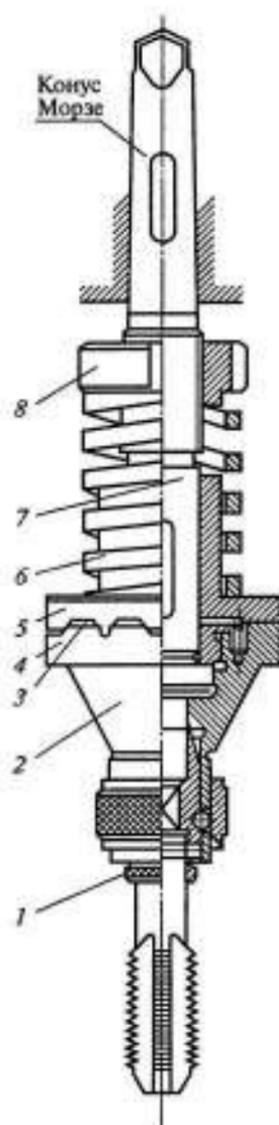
Предохранительный патрон для нарезания резьбы в глухих и сквозных отверстиях:
